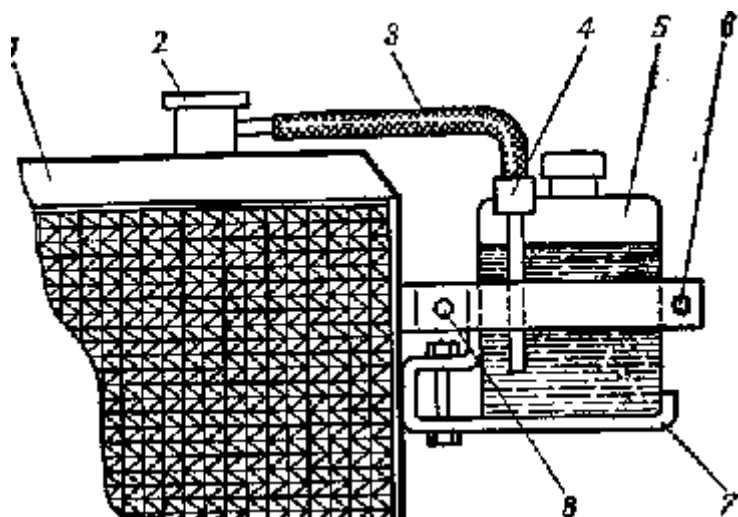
Расширительный бачок из пластмассовой банки: 1 — радиатор; 2 — пробка радиатора; 3 — шланг; 4 — уплотнительная втулка; 5 — банка пластмассовая; 6, 8 — болты крепления; 7 — кронштейн из металлической полосы
